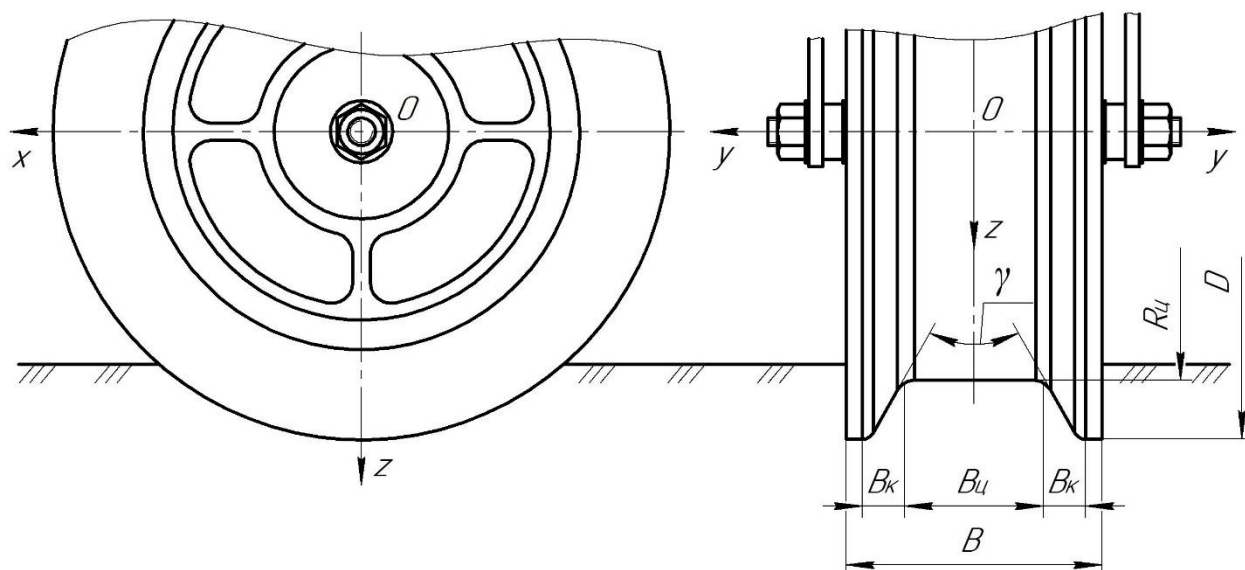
Розрахункова схема поперечного перерізу котка
